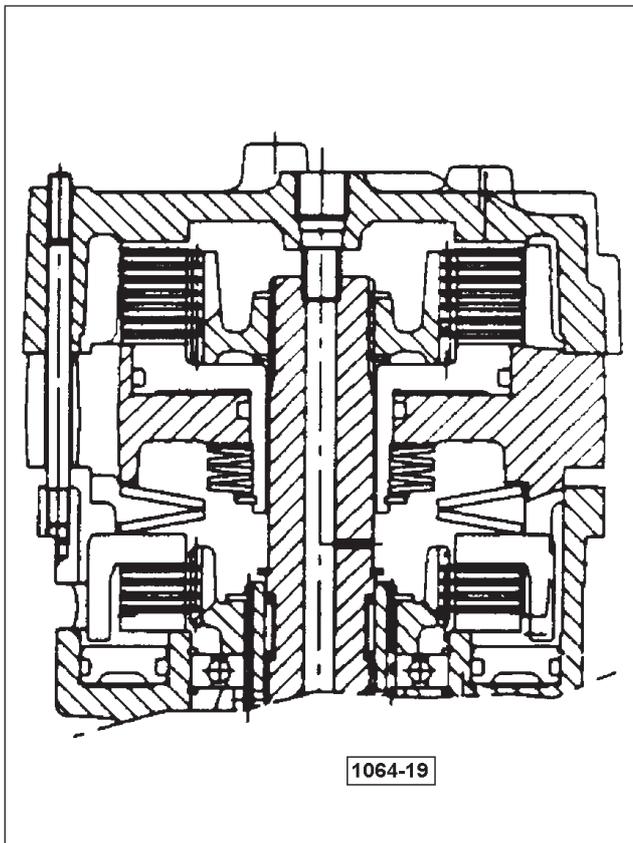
Prémontage des pièces sur l'arbre "MEDIUM".
